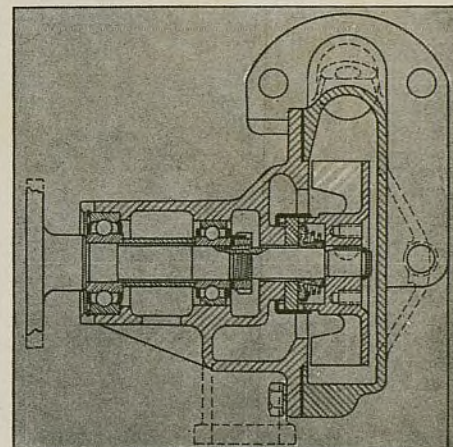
Vista seccional de la bomba de agua sin empaquetadura Cummins
